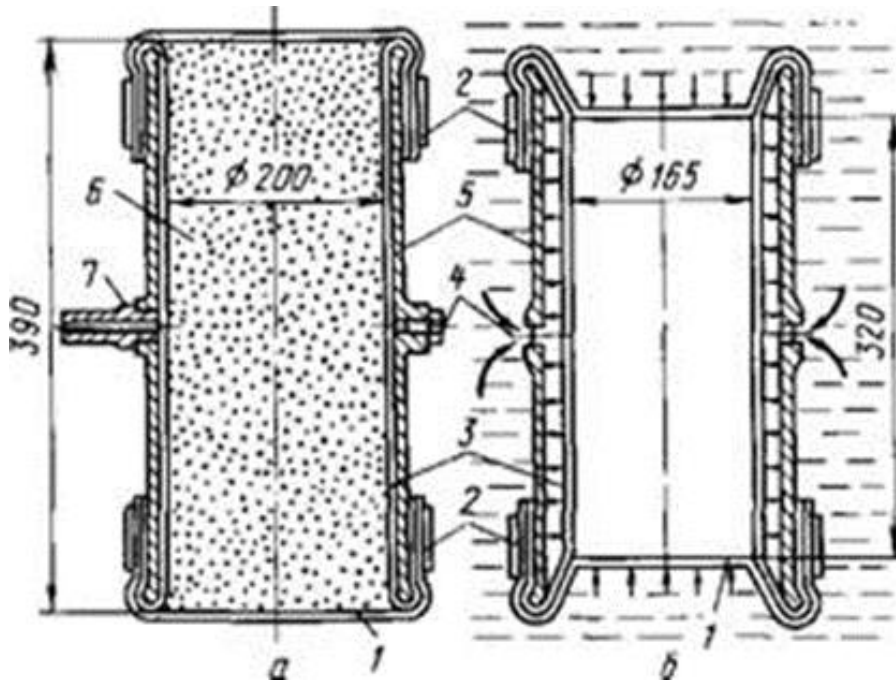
Схематичний розріз прес-форми для гідростатичного пресування циліндричної заготовки:
